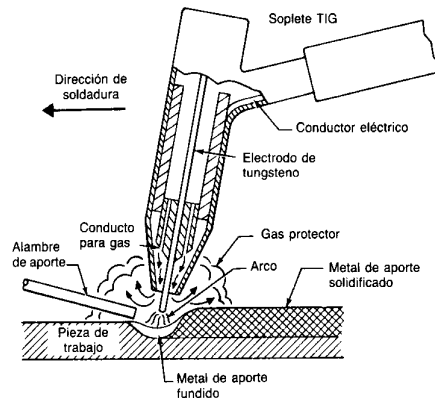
Muestra el proceso de soldadura por arco de tungsteno y gas.
